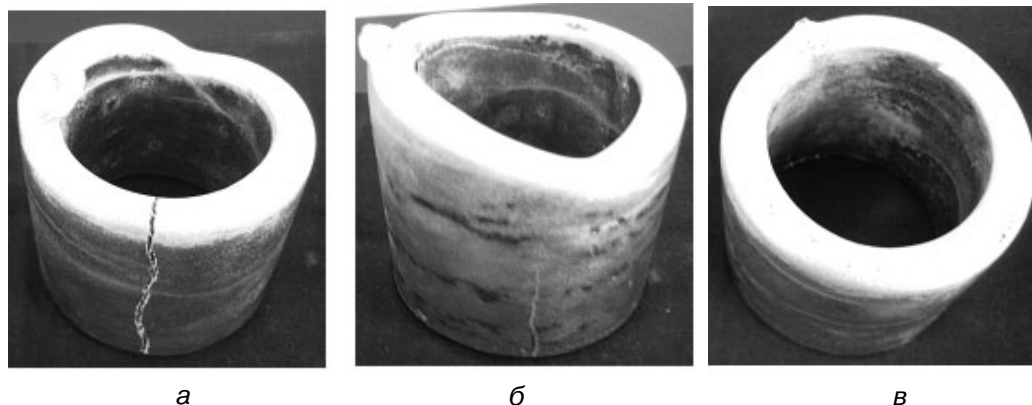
Характерные виды горячих трещин кольцевых проб, изготовленных из высокопрочного алюминиевого сплава марки ВАЛ10: а – сквозная вдоль образующей; б – 1/2 образующей; в – цельная проба
